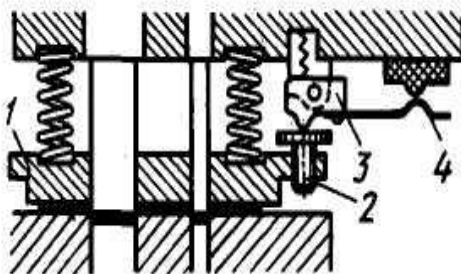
Пристрій для виключення преса при попаданні в штамп двох заготовок: 1— знімач, 2— гвинт, 3— важіль, 4— контактна пластина
